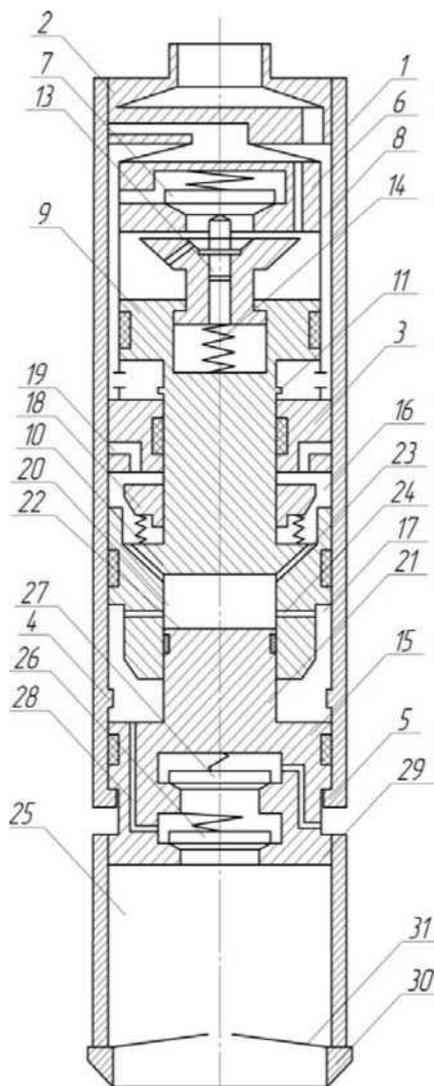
Усовершенствованный гидроударный пробоотборник:
